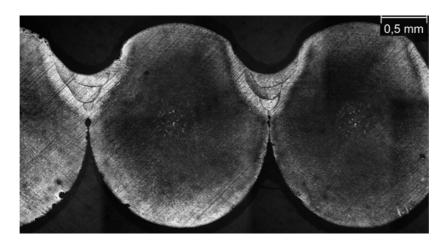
Общий вид области сварного шва пружинно-витого канала, полученного многопроходной сваркой импульсным лазерным излучением
